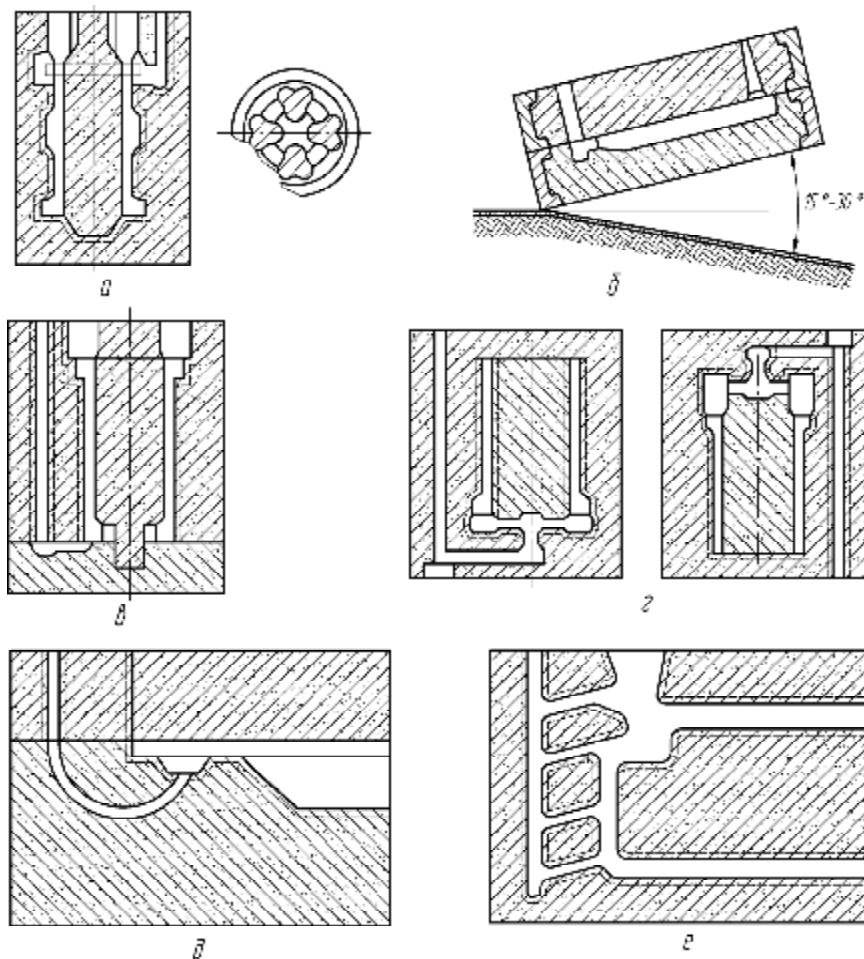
Типовые конструкции литниковых систем для стальных отливок
